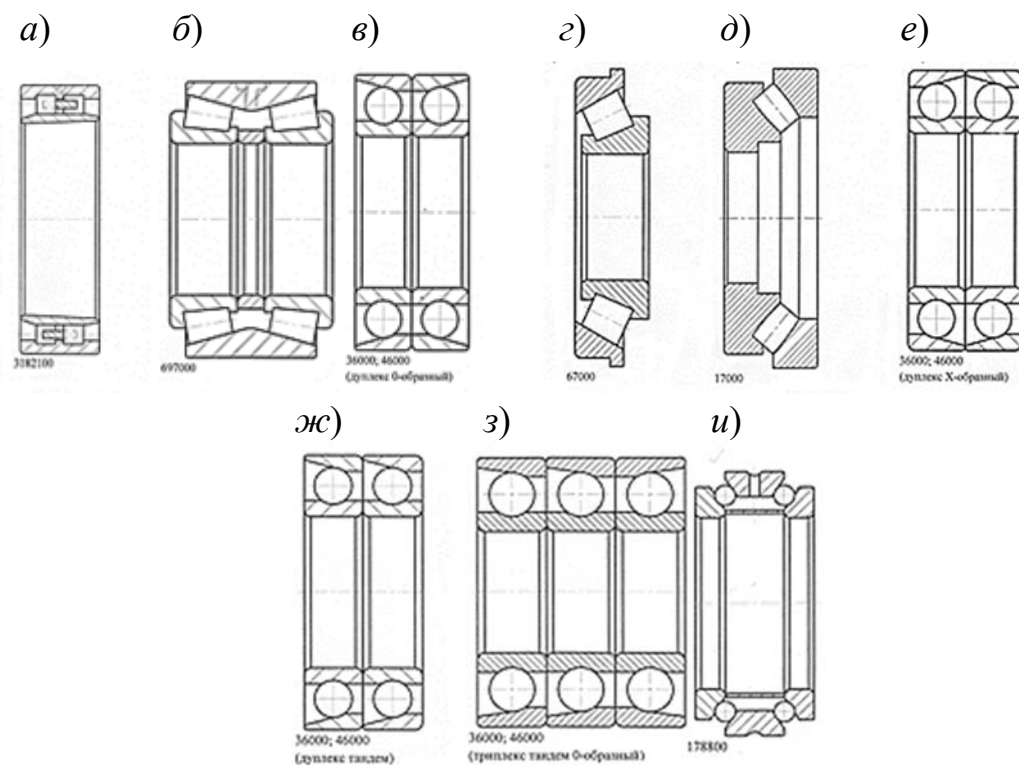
Типы подшипниковых опор шпиндельных узлов
